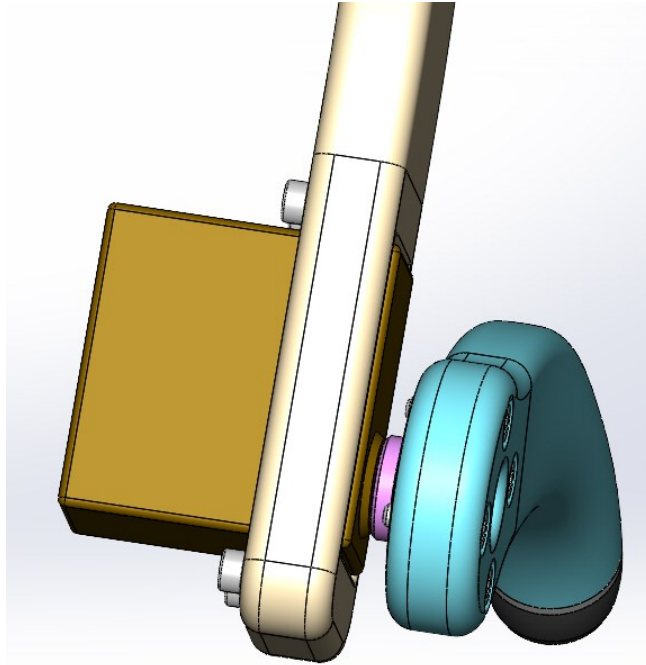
Kluzné ložisko IGUS(IGUS)
